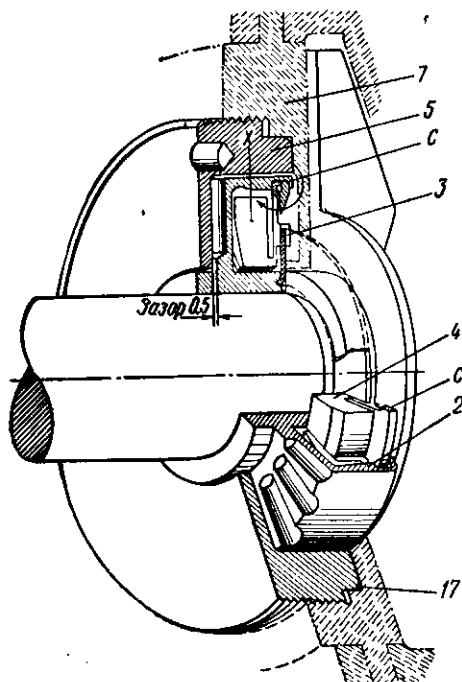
Разрез центробежного насоса для горючего двигателя Р-3395.
